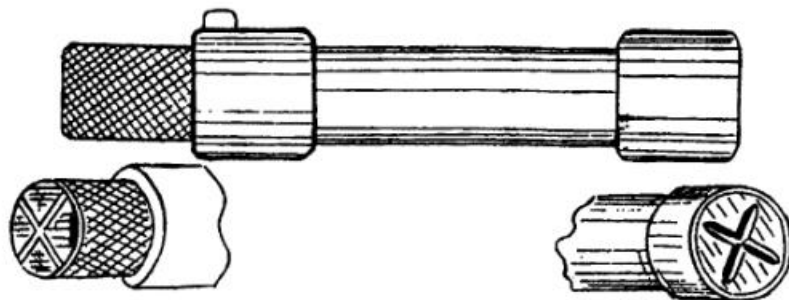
Прибор для проверки прицельных приспособлений ручных гранатометов
